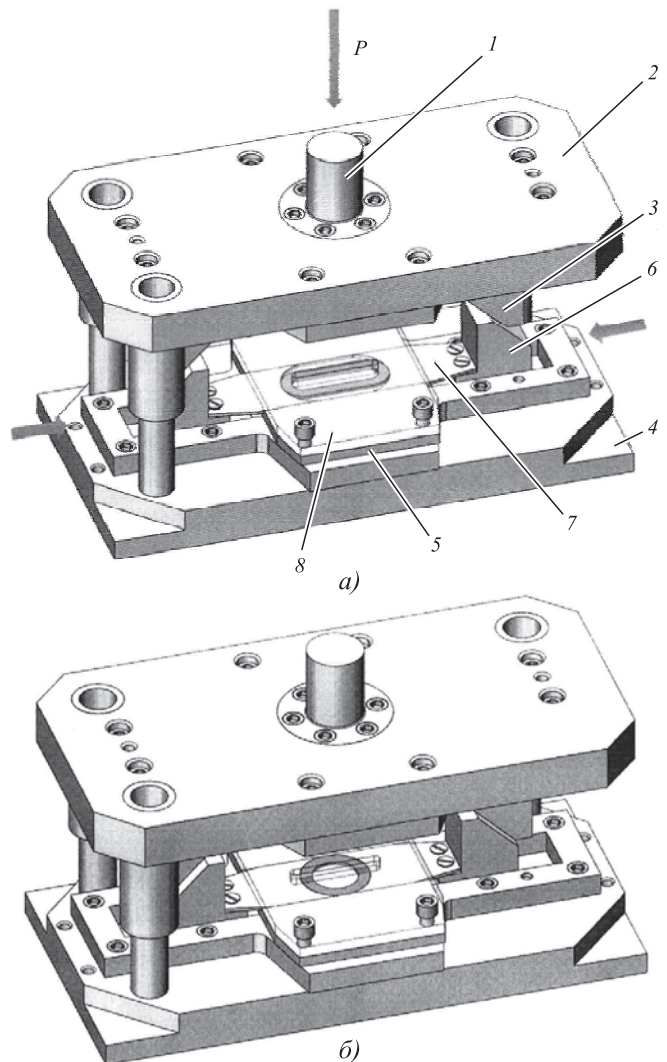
Штамп предлагаемой конструкции в исходном (а) и конечном (б) положениях
